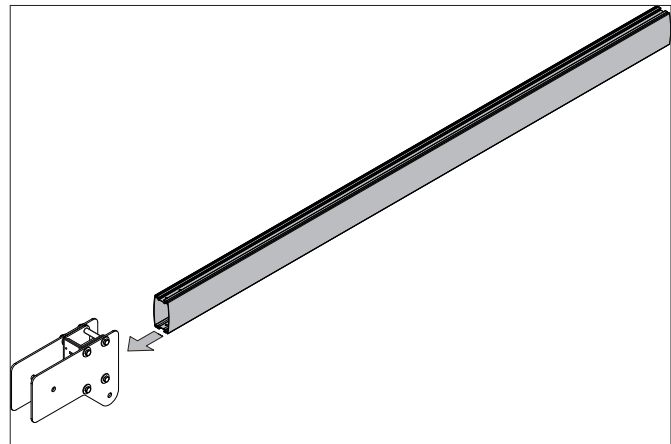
INSTALLAZIONE ASTA FISSA / FIX BAR INSTALLATION
